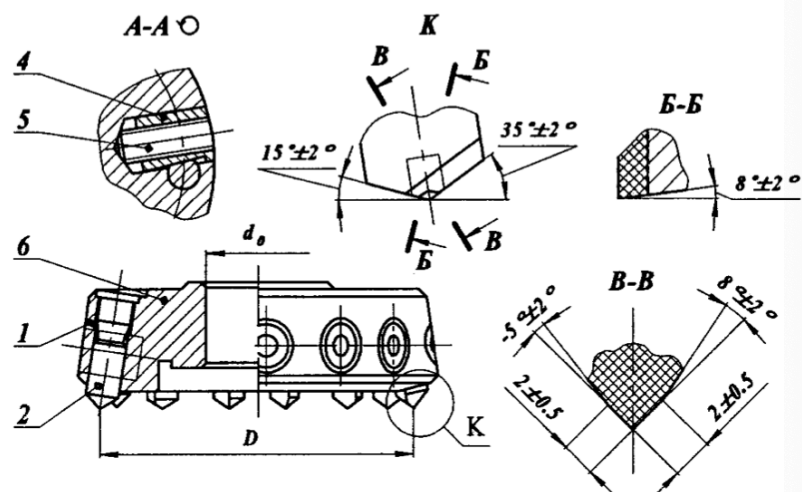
Багато зуба торцева фреза з ножами з композиту
